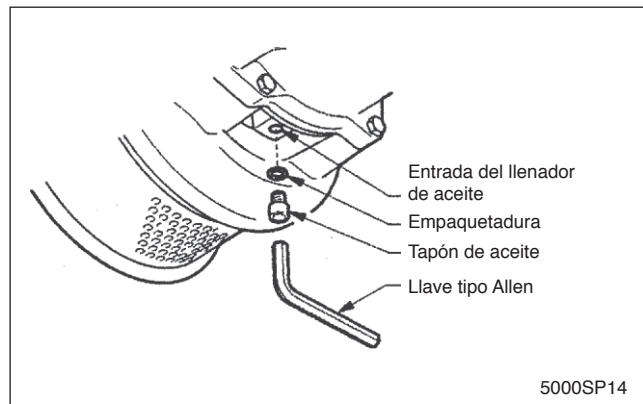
INSPECCIÓN DEL LUBRICANTE
